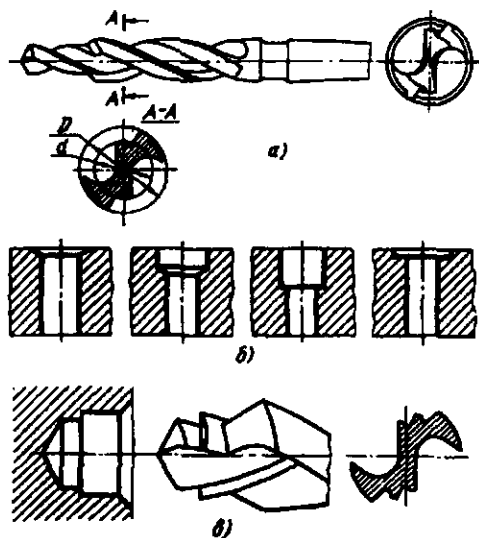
Схемы обработки отверстий комбинированными сверлами: а – четырехленточное сверло; б – примеры обработки четырехленточными сверлами; в – обработка отверстия шестиленточным сверлом
